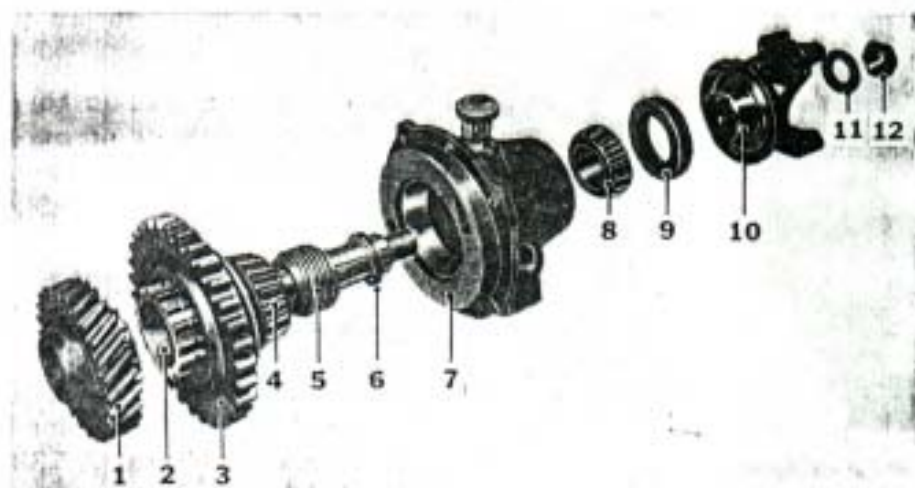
Despiece del conjunto extensión de salida al eje trasero.
